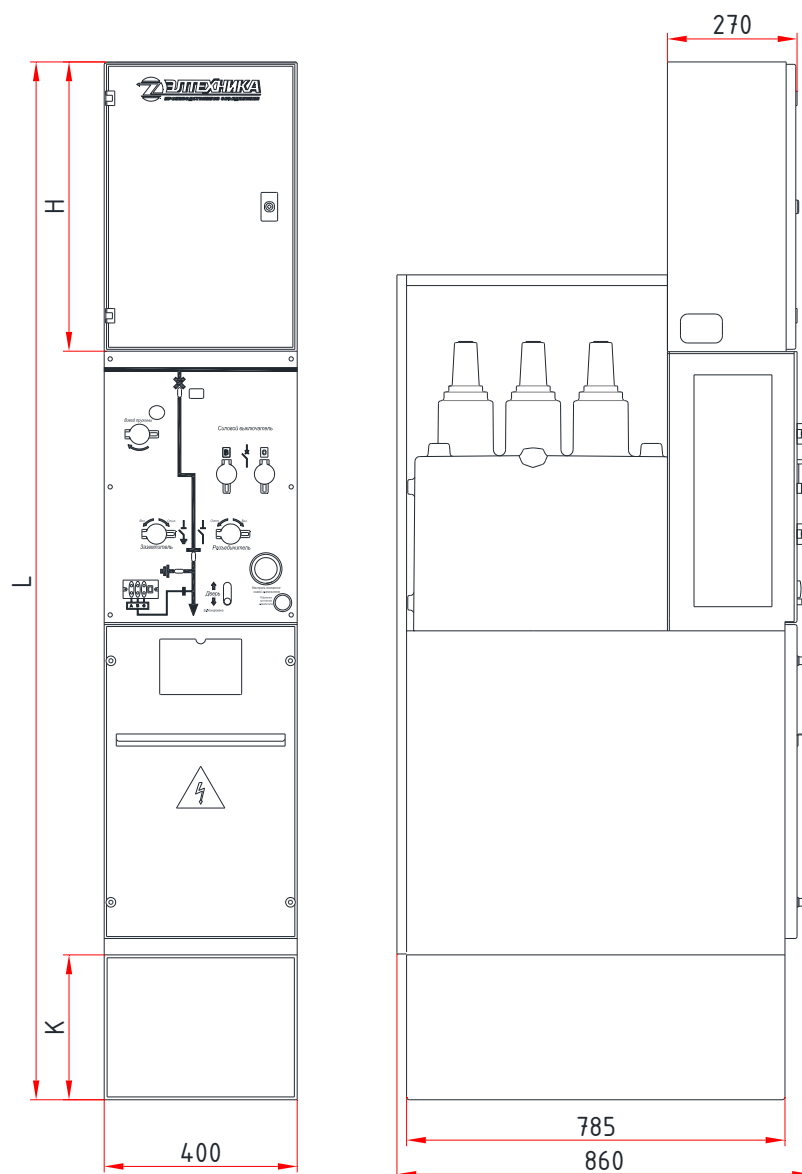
Габаритные размеры шкафов КРУ базовой конструкции на номинальный ток 630А.
